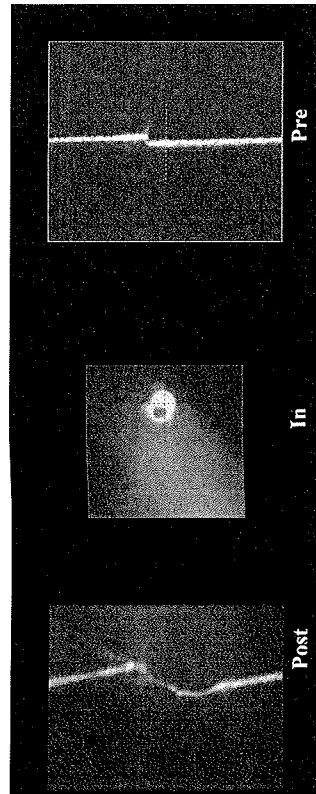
Schweißen eines Testbauteils (Messung S061, Bild-Nr. 71).
